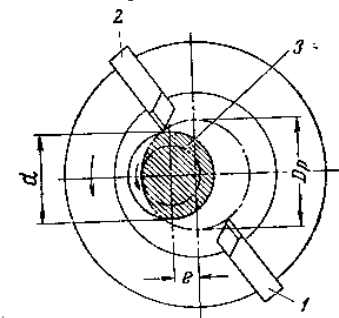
Дуга контакта и смещение осей при вихревом фрезеровании резьбы:
